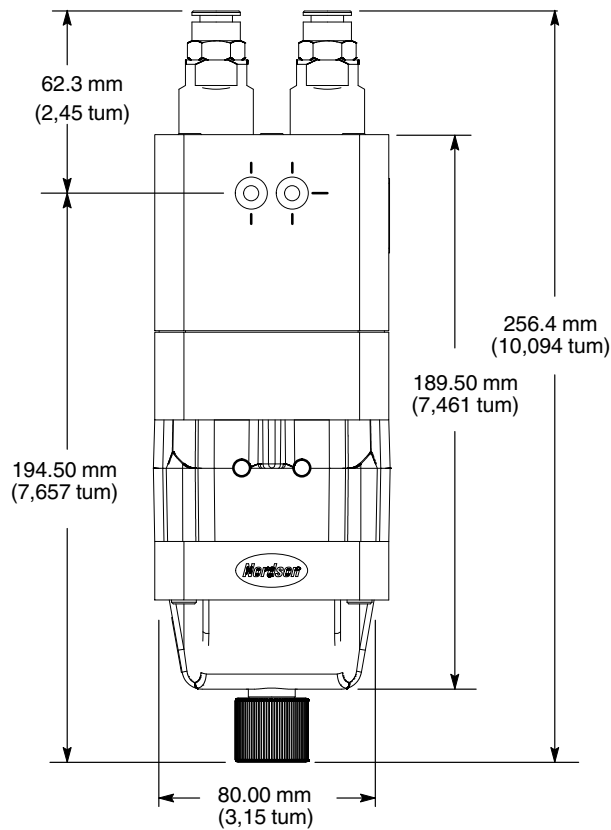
Dimensioner Prodigy HDLV-standardpump
